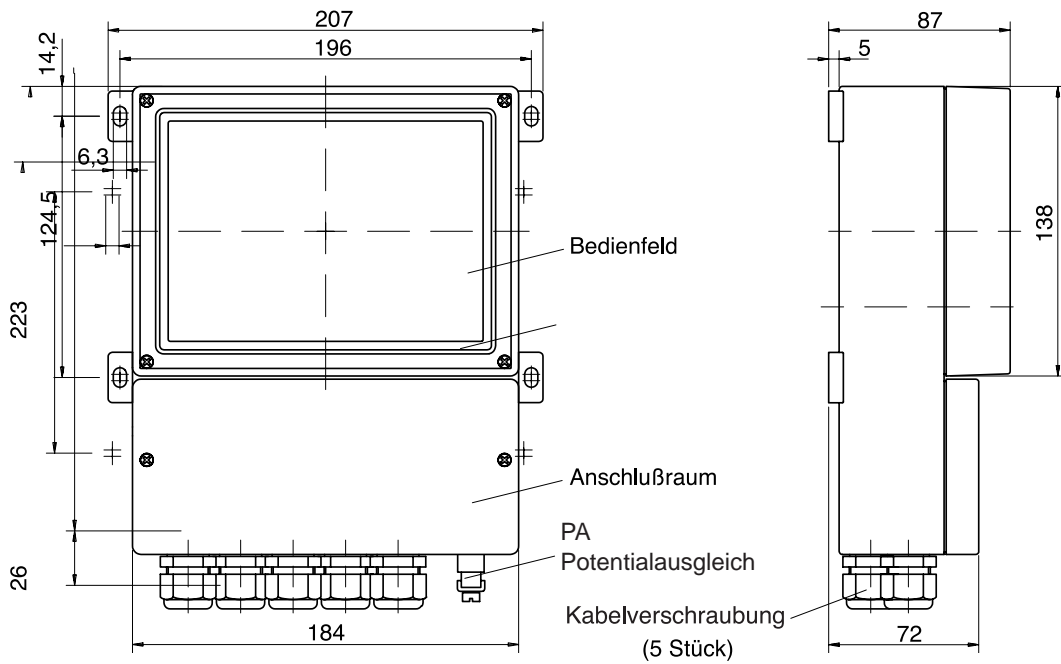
Maßzeichnung pH Transmitter 2220(X)
